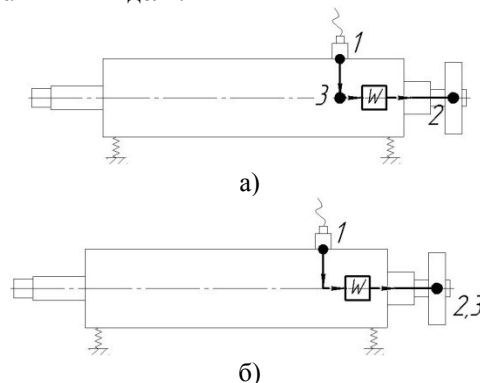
Схема измерения для оценки погрешности изготовления и сборки ШУ на опорах качения (а) и колебаний шпинделя (б): 1 – точка измерения вибраций корпуса; 2 – точка расчета колебаний оси шпинделя (оправки); 3 – точка приложения единичной гармонической силы
